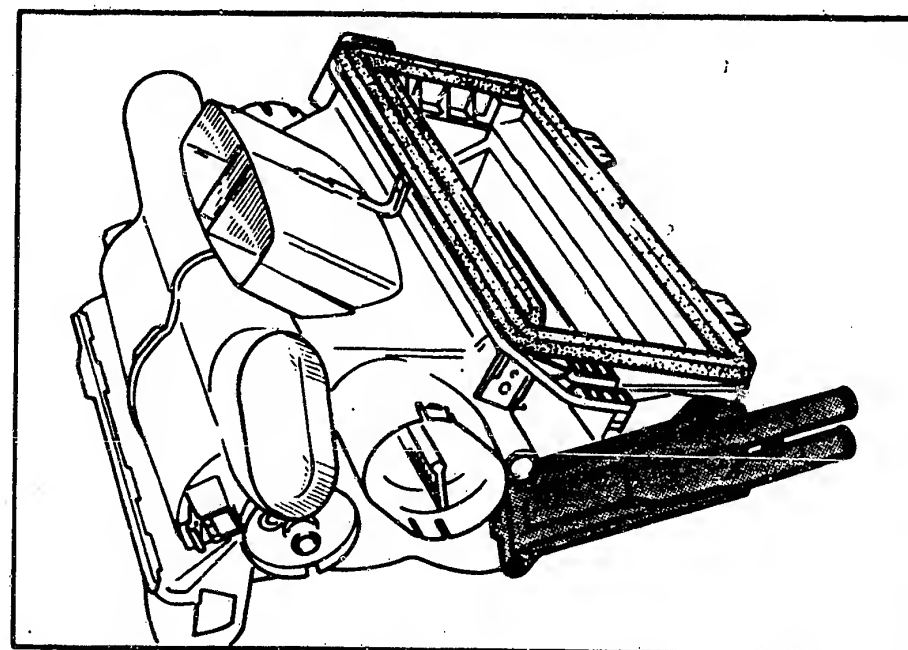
Das Heizungsgehäuse mit Wärmetauscher aus Aluminiumrohren ist in der Mitte unter dem Armaturenbrett eingebaut.
